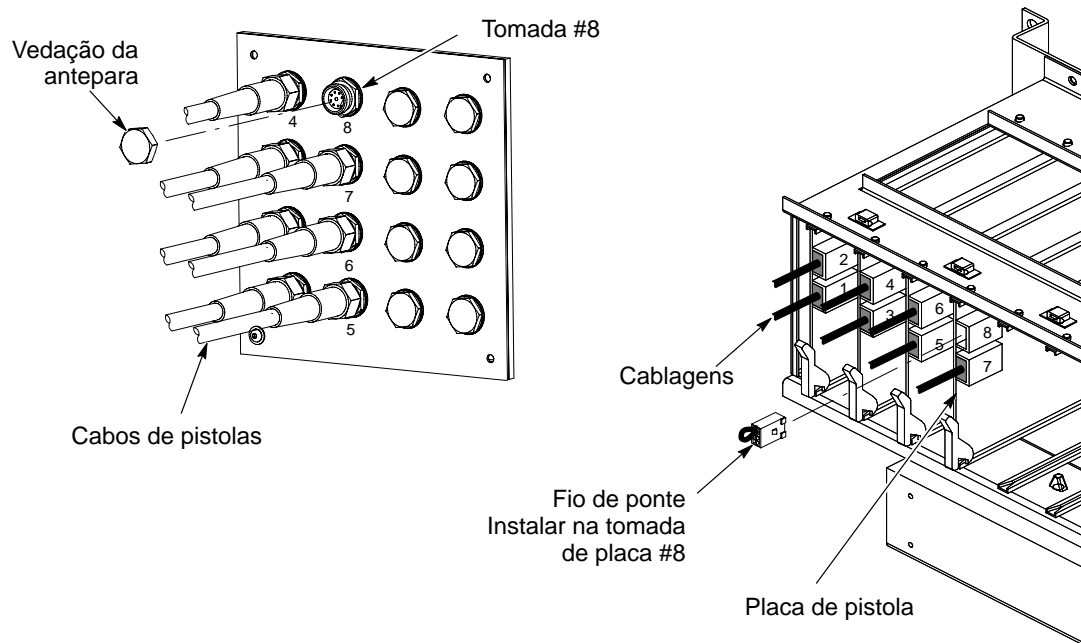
Instalação de vedações e fios de ponte – Exemplo mostrando um sistema de 8 pistolas utilizando 7 pistolas
